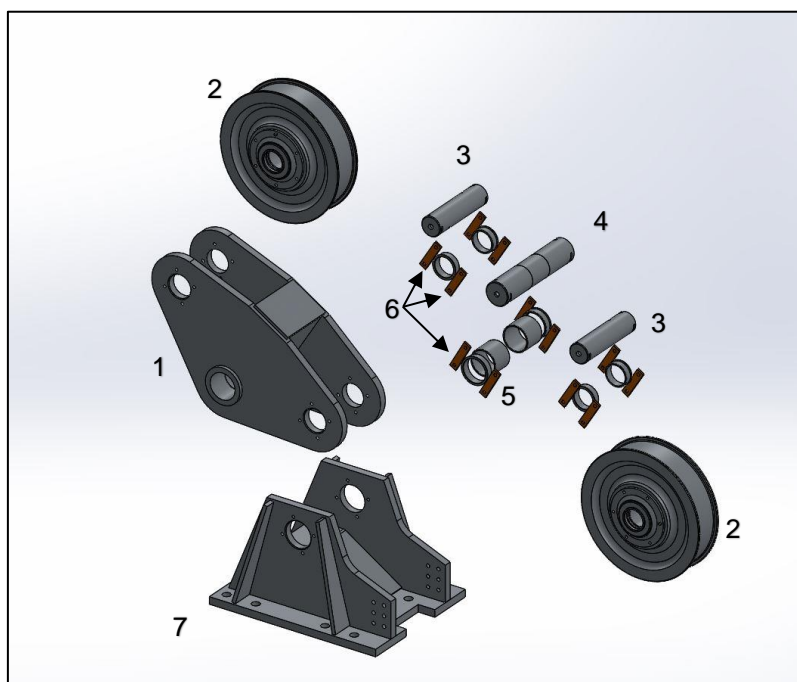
Vista do balancim explodido, componentes do conjunto do balancim.
